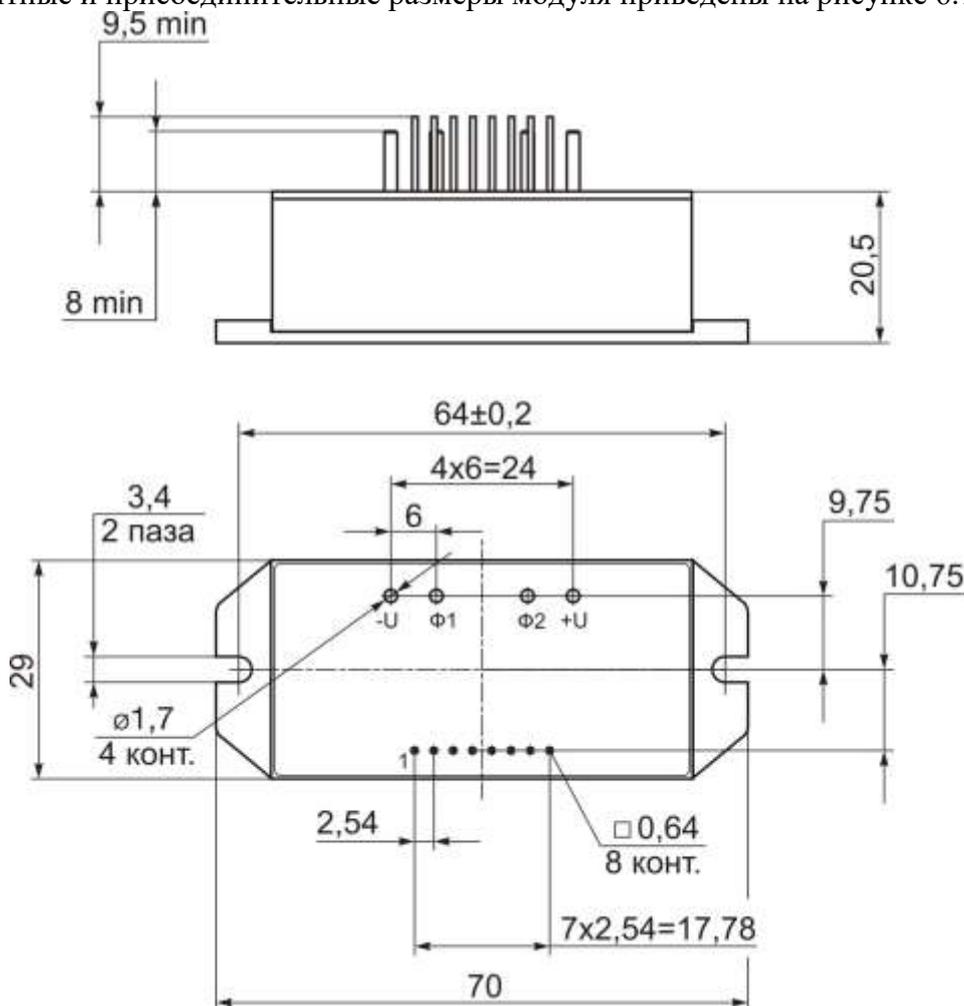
Габаритные и присоединительные размеры модуля
